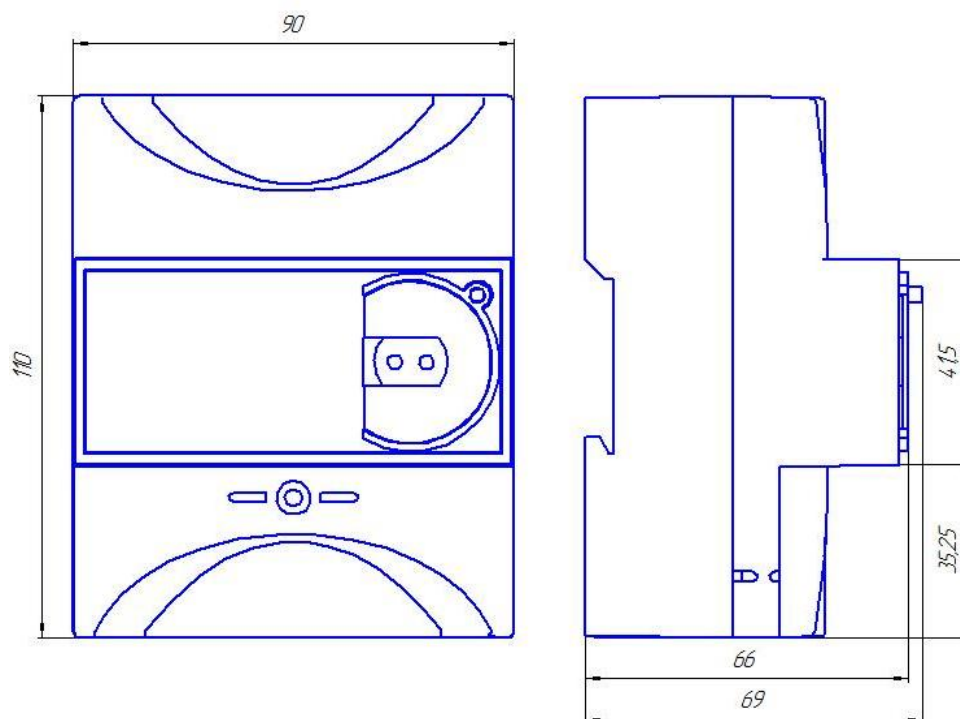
Габаритный чертеж и установочные размеры счетчиков МАЯК 101АТД
